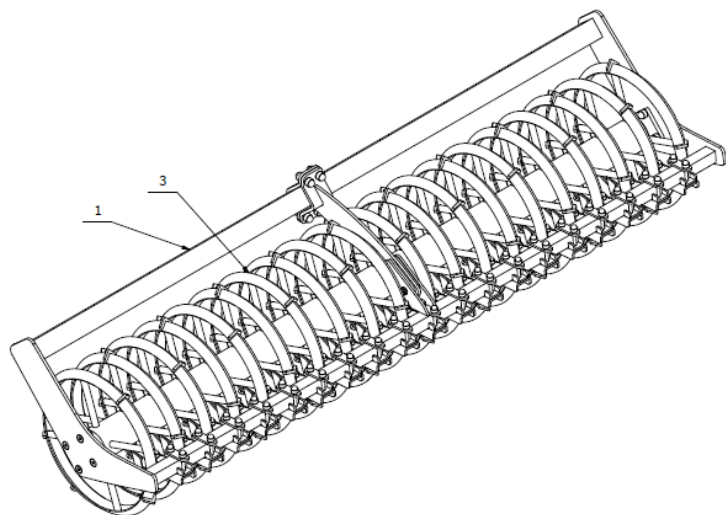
Wał pierścieniowy Ø500mm - mocowanie łózyska.
